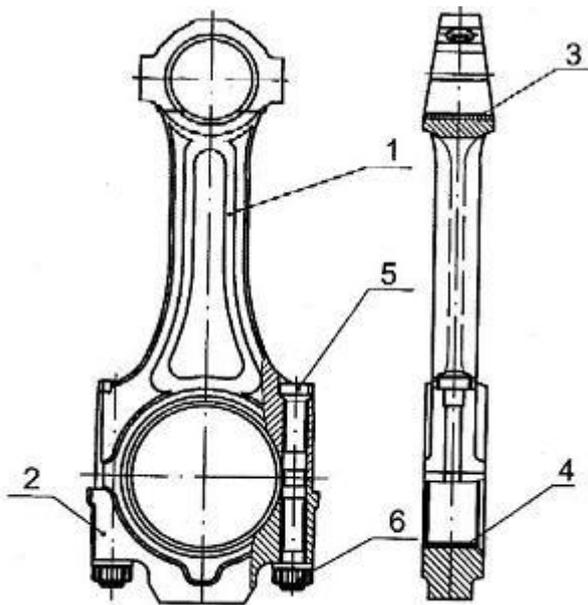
Шатун: 1 — стержень шатуна; 2 - крышка шатуна; 3 - втулка верхней головки-шатуна; 4 - вкладыш нижней головки шатуна; 5 - болт крепления крышки шатуна; 6 - гайка болта крепления крышки шатуна.
